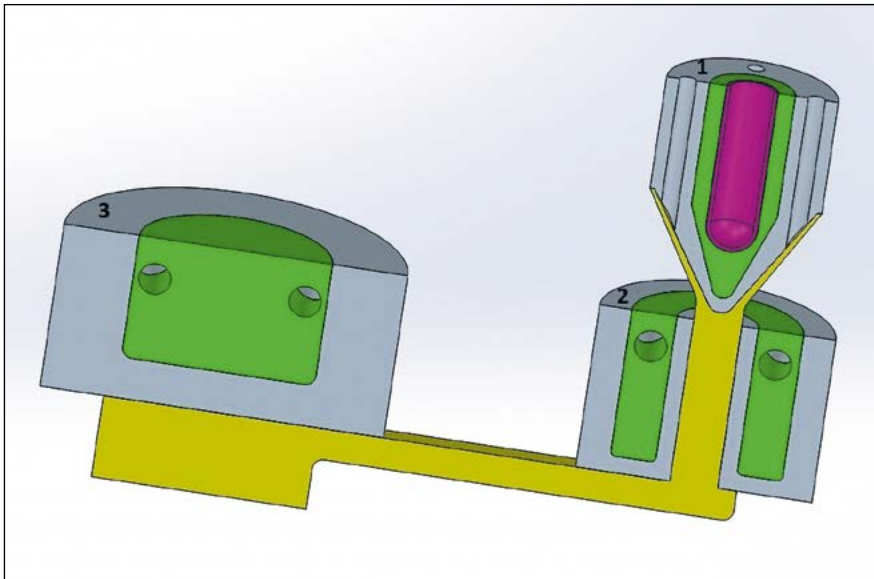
Gießsystem eines Dreiplattenwerkzeuges mit Angusseinsätzen in Mecobond®-Bauweise
